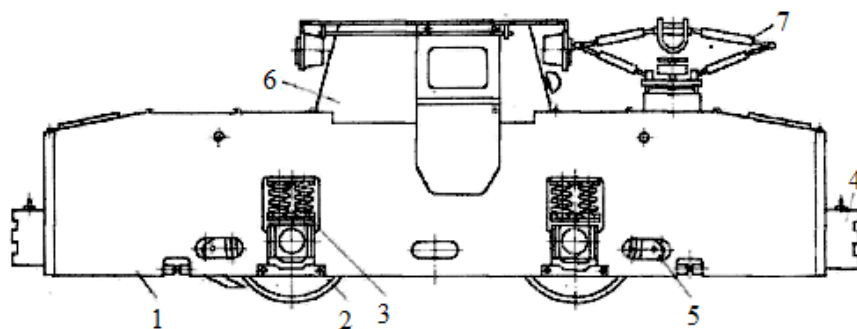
Схематическое устройство электровоза: 1) рама; 2) колесная пара; 3) рессорная подвеска; 4) сцепное устройство; 5) тормозная система; 6) кабина; 7) токоприемник
